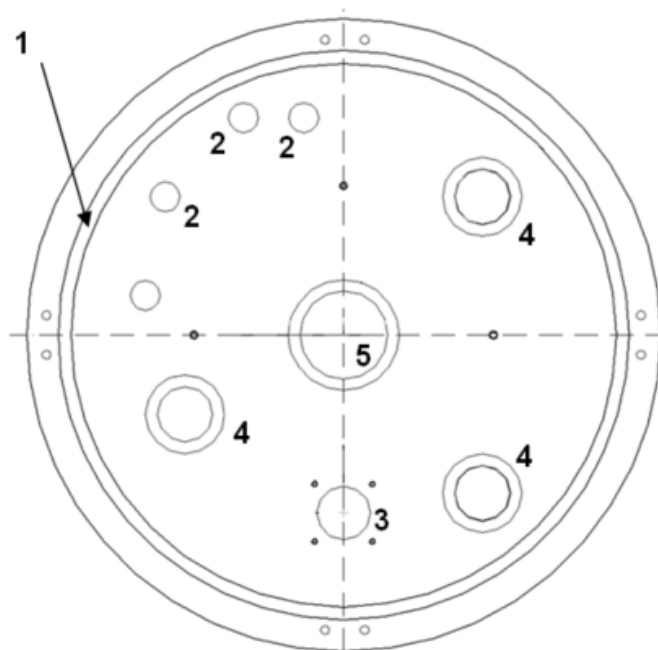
Схема присоединительных отверстий и пазов основного фланца камеры
